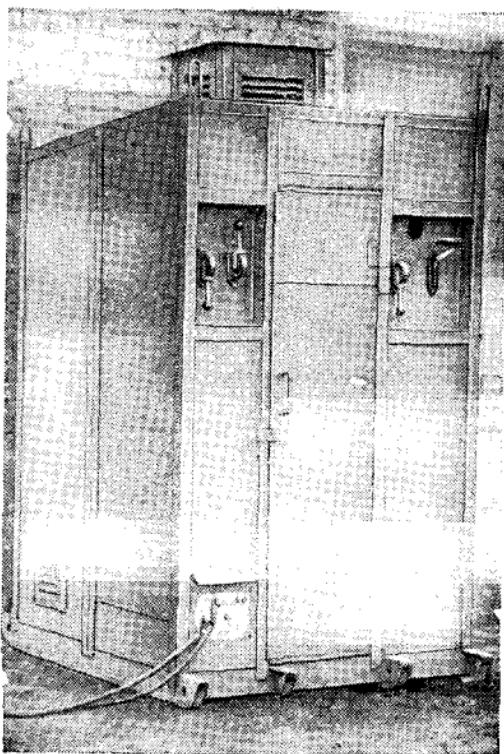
Передвижной сварочно-трансформаторный пункт ПСТТ-3
